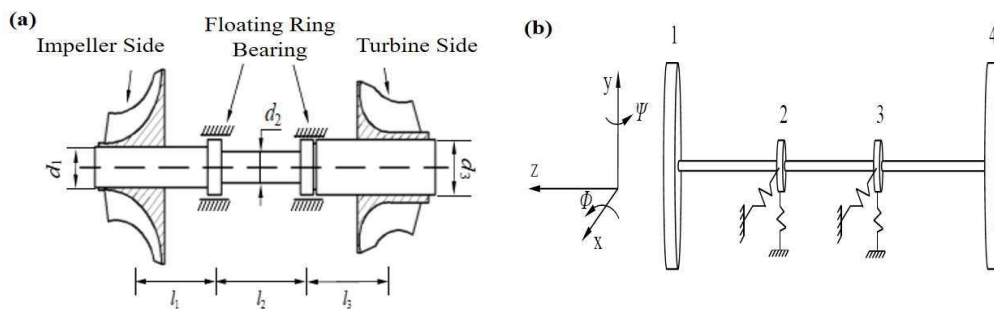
Принципова схема та механічна модель роторно-підшипникової системи турбокомпресора: (а) – принципова схема; (б) – механічна модель [70]
